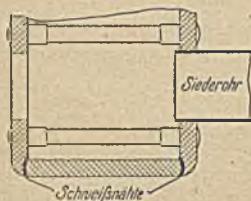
Die Schweißstellen des Umlaufbleches.
